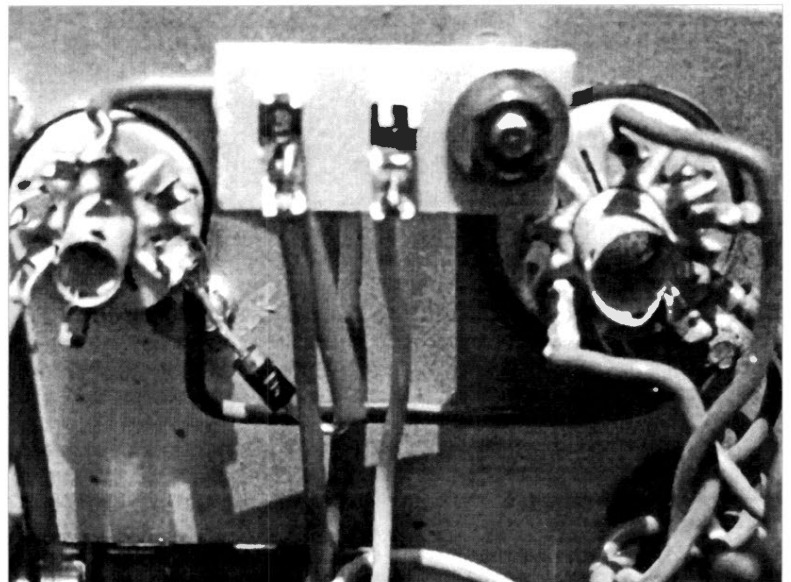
Oben ist gut die „Modernisierung“ mit einer Siliziumdiode zu erkennen.
